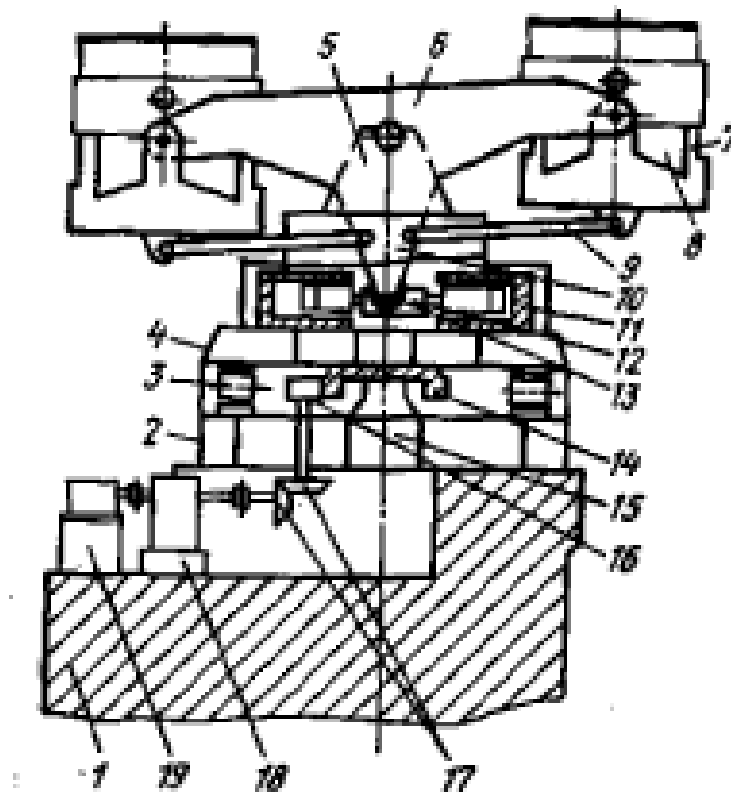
Сталеразливочный стенд конструкции ПО УЗТМ
